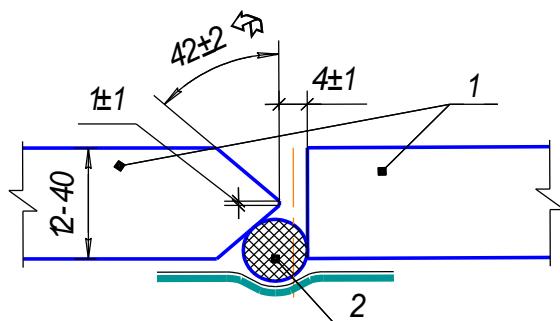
Геометрические параметры стыкового шва с V-образной разделкой кромок, выполненного автоматической сваркой под флюсом по ручной подварке корня шва (АФ+РД)
